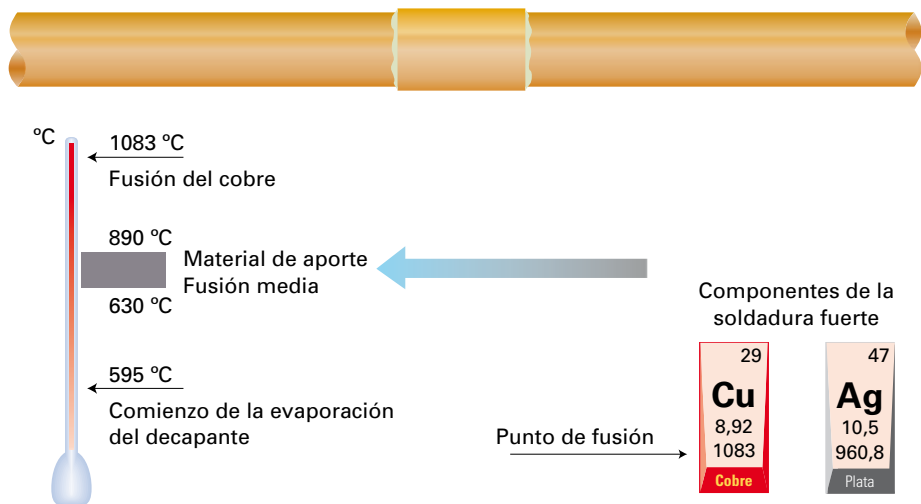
Intervalos de fusión en la soldadura fuerte
